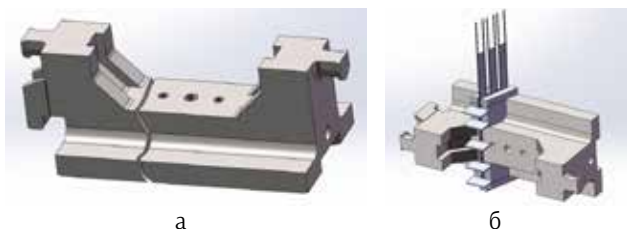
Ремонт корпуса бойка к прессу усилием 5000 тс с простой трещиной, расположенной в одной плоскости: а – схема развития трещины в корпусе бойка; б – схема электрошлаковой сварки корпуса бойка при его ремонте
